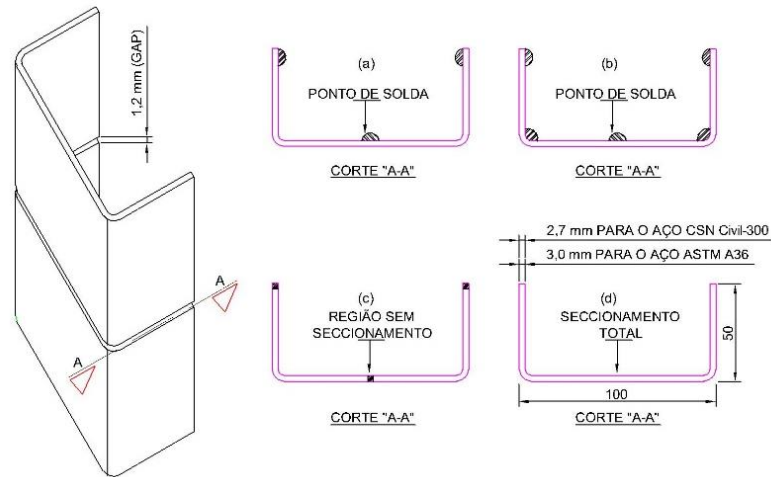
Montagens das juntas preparadas para o processo de soldagem, representadas pelos cortes "A-A": (a) junta com três pontos de solda, (b) junta com cinco pontos de solda, (c) junta experimental e (d) junta normalmente seccionada.
